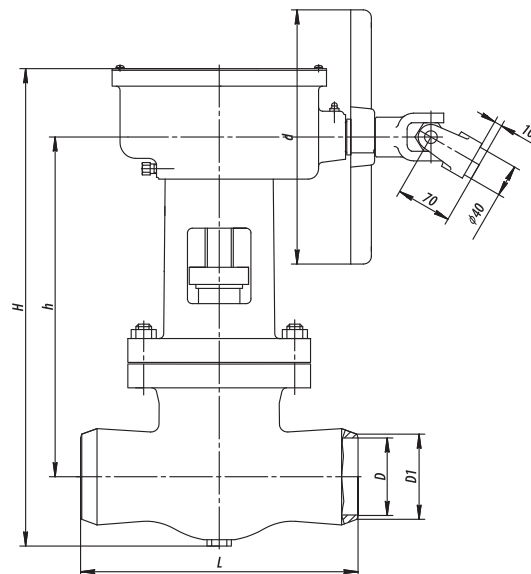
Задвижка DN80-100 с коническим редуктором
